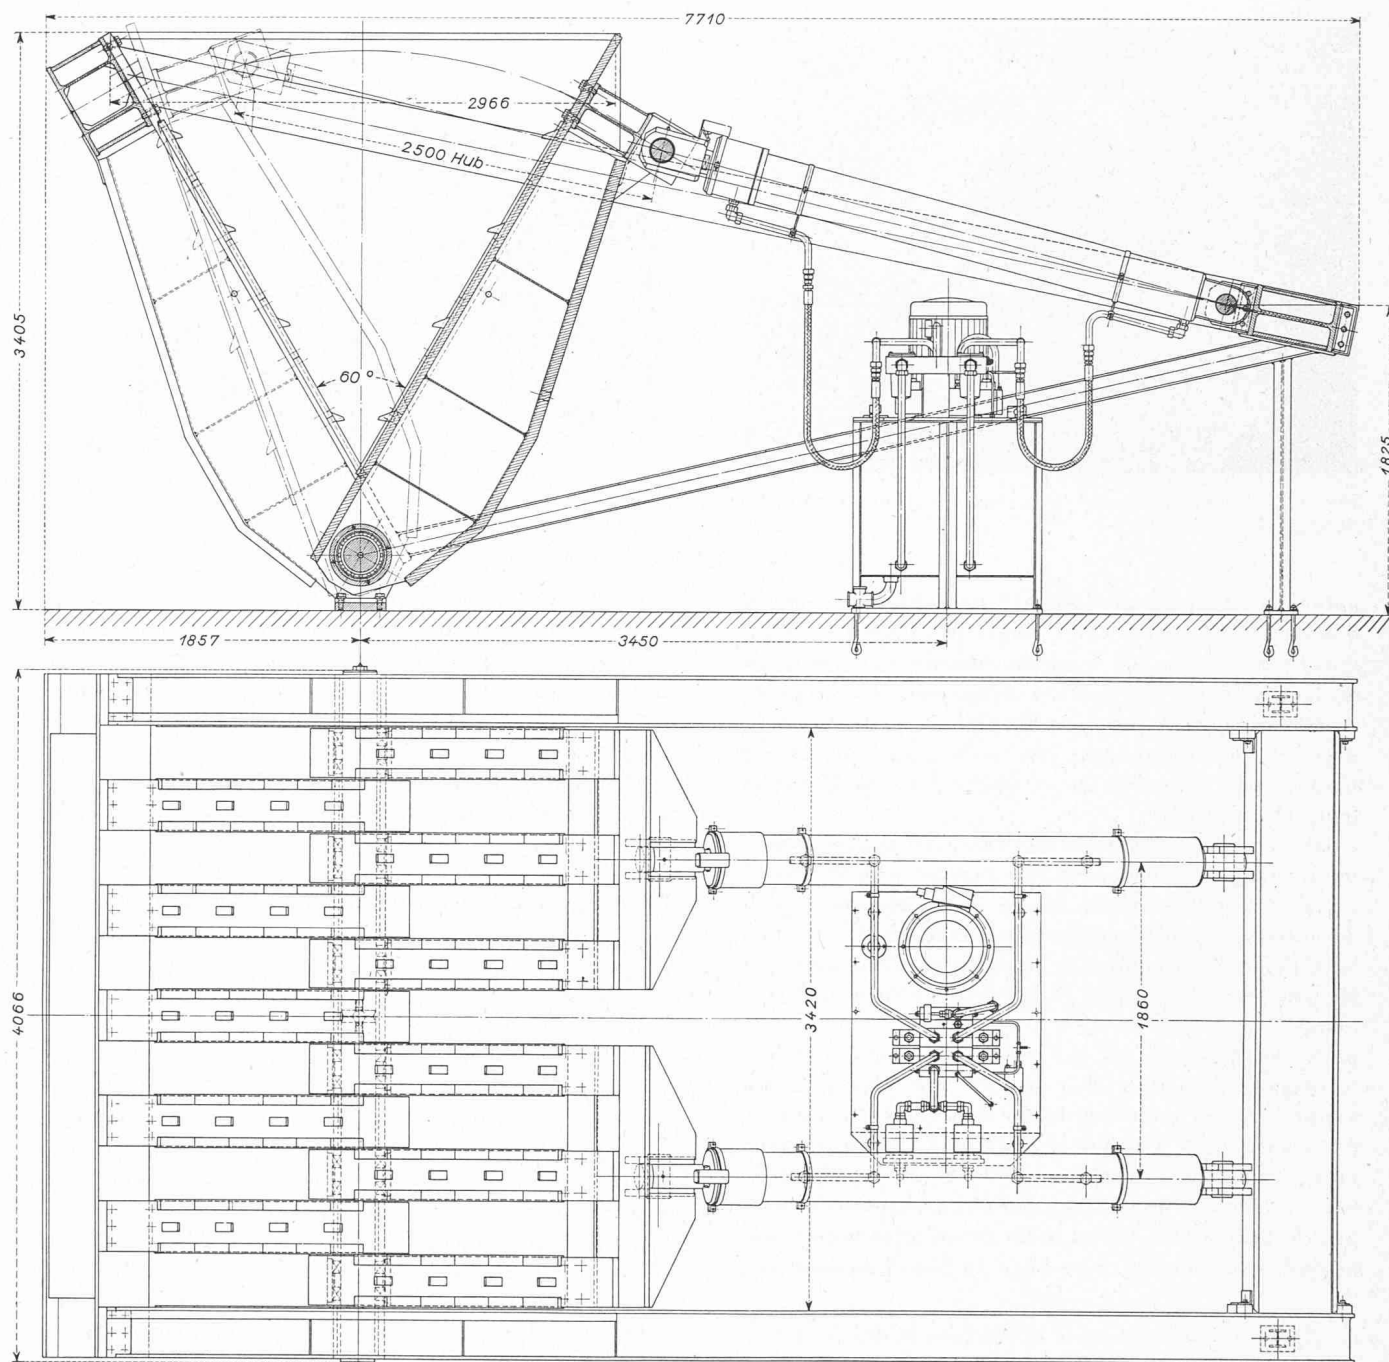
Section longitudinale et vue en plan du broyeur-hacheur pour déchets encombrants.
